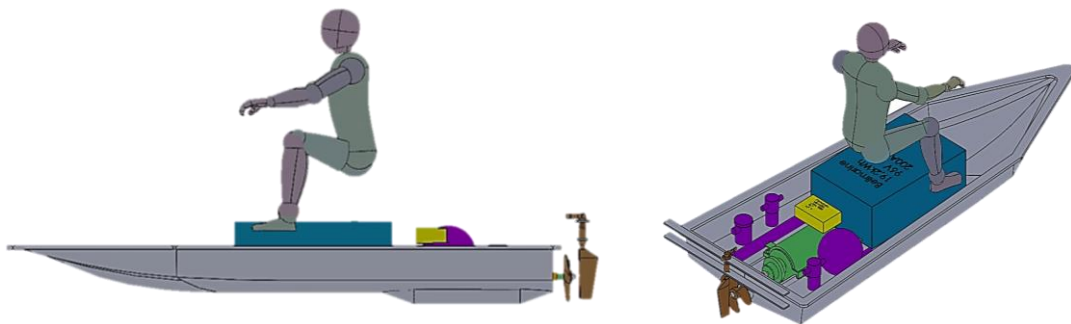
Diseño con motor Drive Master de Bellmarine (Fuente: elaboración propia).
